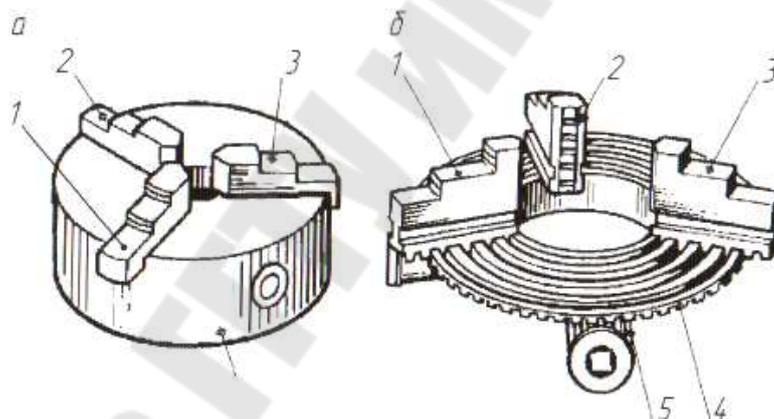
Трехкулачковый самоцентрирующий патрон: *a* – общий вид; *б* – устройство; 1– 3 – кулачки; 4 – диск с коническим зубчатым венцом и спиральной нарезкой; 5 – приводное коническое зубчатое колесо; 6 – корпус
